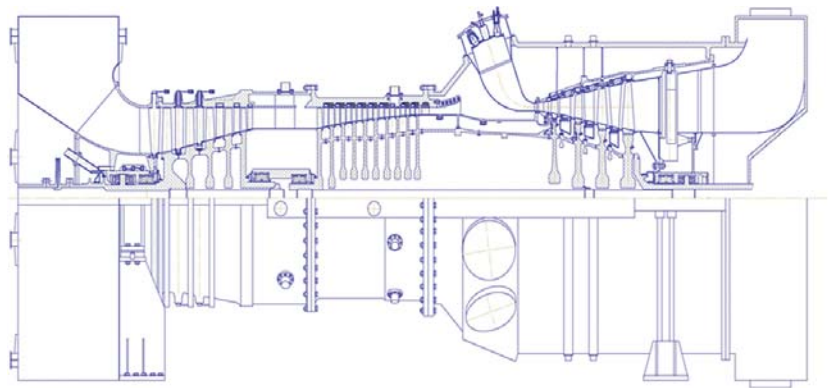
Двухвальный осевой компрессор ПГУ с частичным паротурбинным приводом
